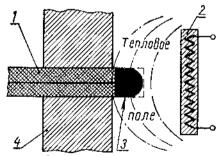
Схема образования торцового шва в тепловом поле ленточного нагревателя:
